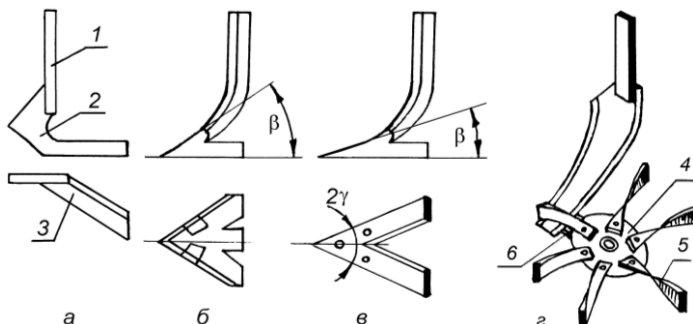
Полочные рабочие органы: *a* – односторонняя плоскорежущая лапа; *б* – стрелчатая универсальная лапа; *в* – стрелчатая плоскорежущая лапа; *г* – пропалочный диск; 1 – стойка; 2 – щека; 3 – лезвие; 4 – диск; 5 – нож; 6 – кронштейн
